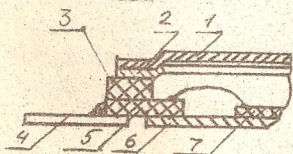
Металлокерамический корпус типа 5: 1 - крышка; 2 - ободок; 3 - рамка; 4 - вывод; 5 - основание; 6 - дно; 7 - подложка
